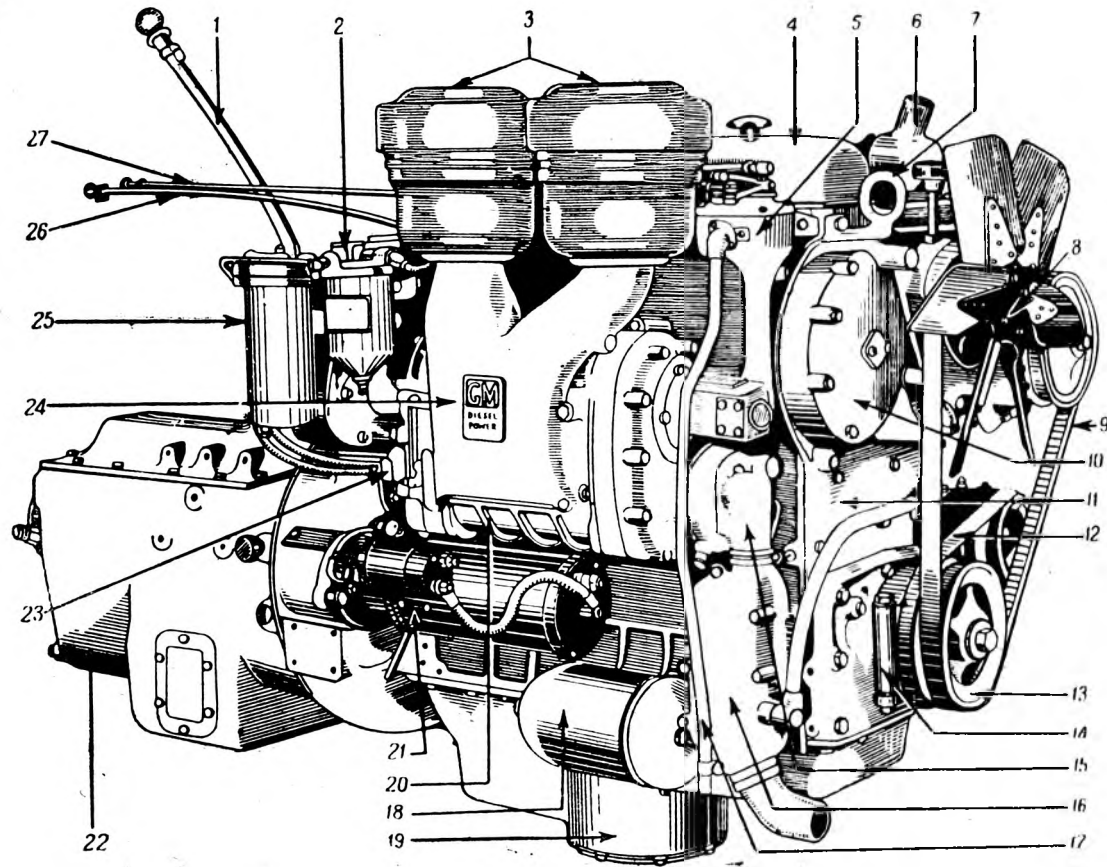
Двигатель Джизмси (вид с правой стороны):
